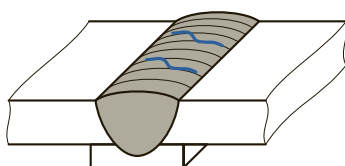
Поперечные трещины в металле сварного шва
